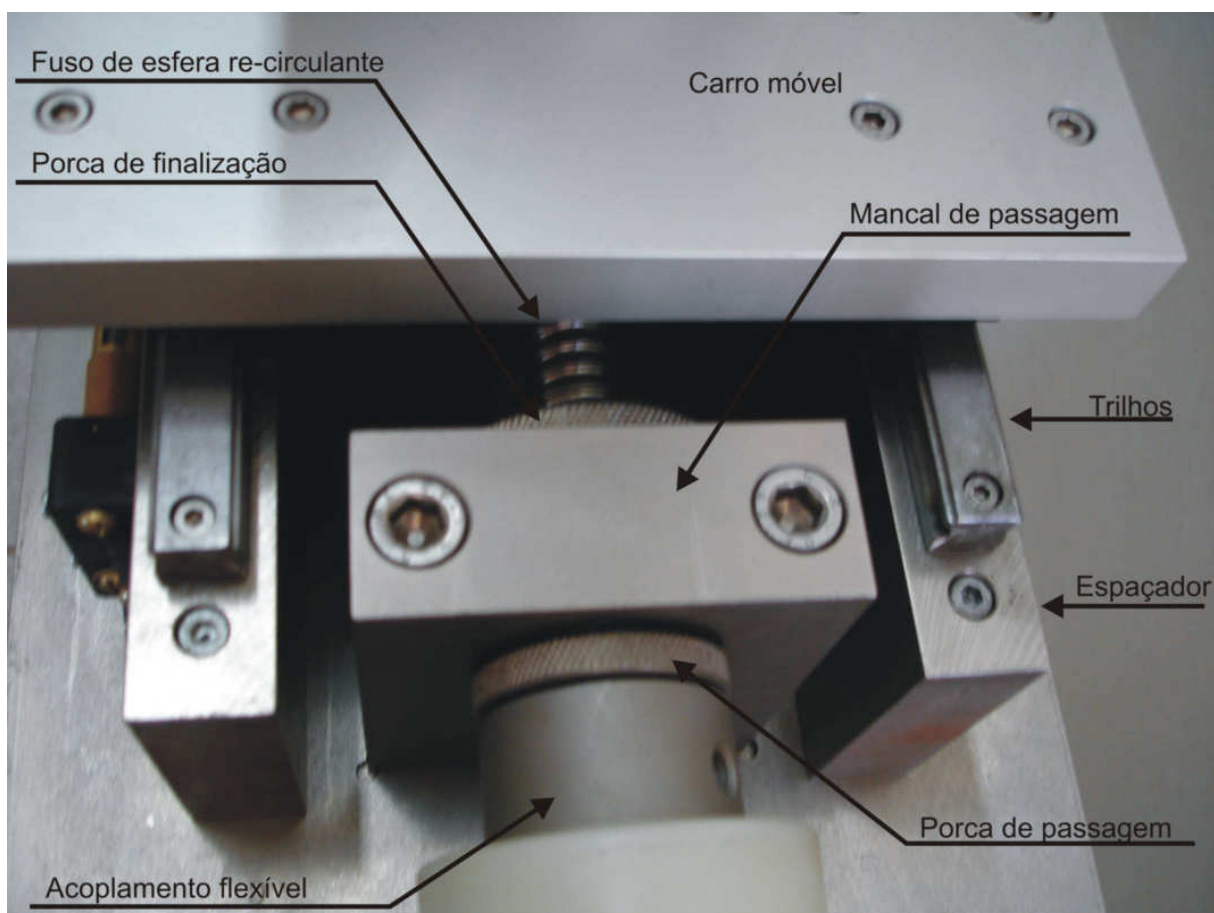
Mancal de passagem, com o acoplamento ao eixo do redutor; parcialmente pode ser visto o fuso de esfera re-circulante.
